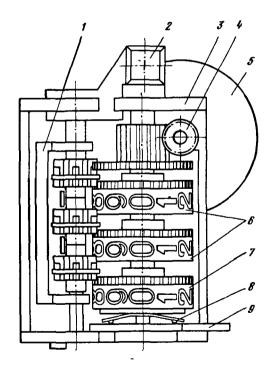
Счетчик расхода магнитной ленты: 1— рычаг сброса; 2— кнопка сброса; 3— корпус; 4— однозаходный червяк; 5— шкнв; 6, 7— цифровые барабаны; 8— контакт; 9— печатная плата
